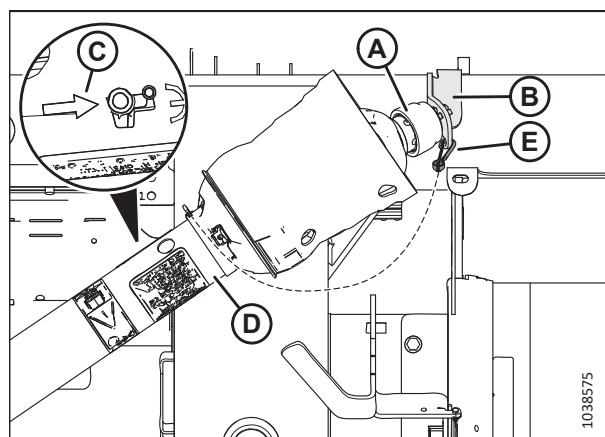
Додатковий щиток приводного вала для роботи на схилах
